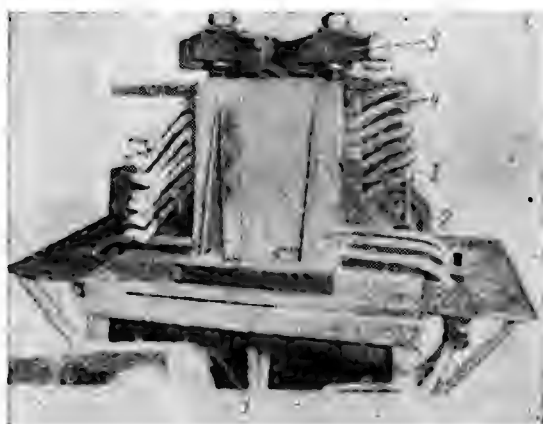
Многоарусный пресс для опрессовки изоляции катушек:
